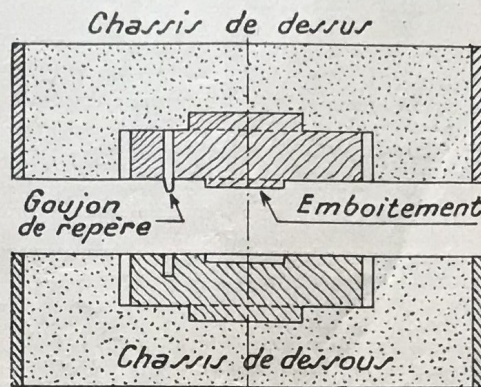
Moulage d'un engrenage hélicoïdal.
